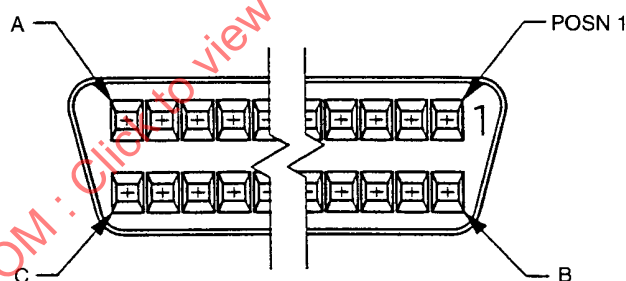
Face d'accouplement d'un connecteur avec contacts femelles
